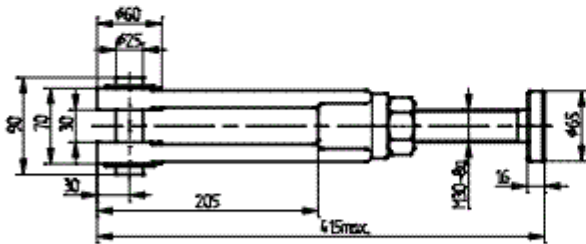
Соединительная тяга для механизмов М30-4000-97К (в комплекте - вилка и шток)
